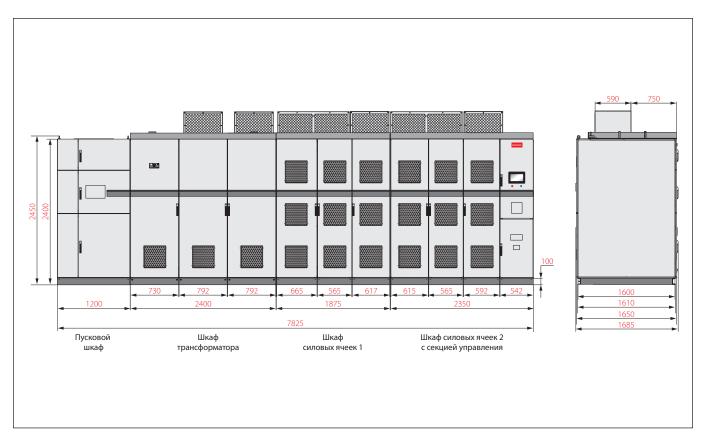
Корпус RA04 на напряжение 6 кВ
